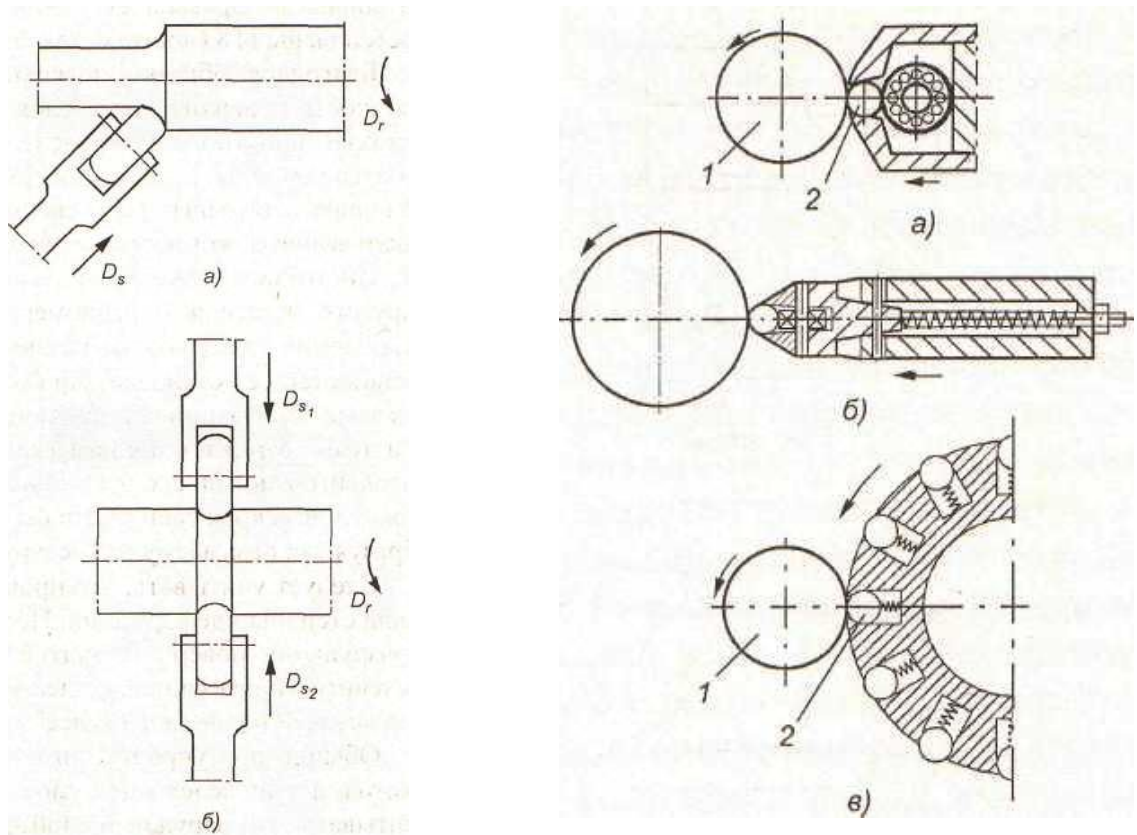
Схемы обкатывания вала роликами и шариками:
